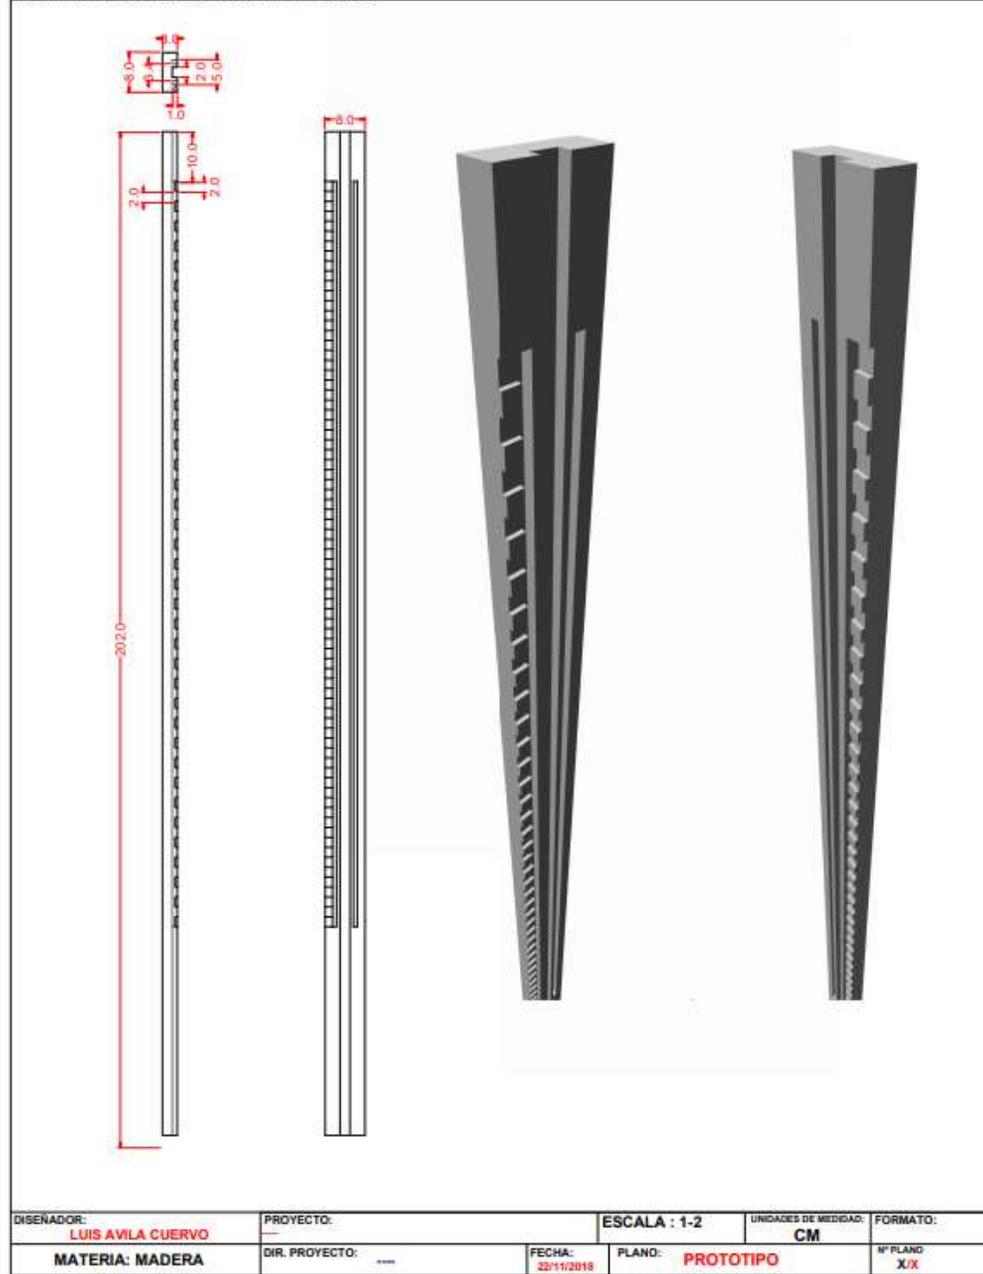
Planos de la Propuesta Luis Ávila (2016)
